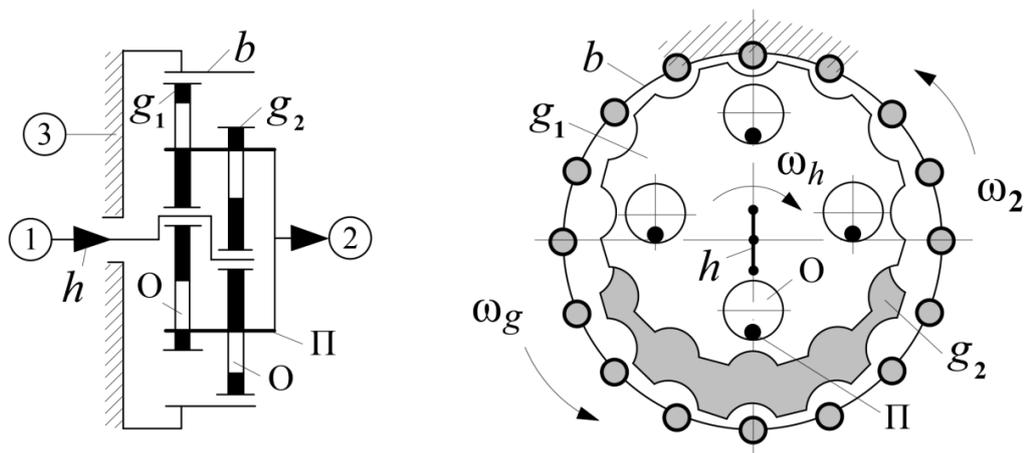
Планетарно-кривошипный механизм цветочного зацепления с двумя оппозитными сателлитами (звездочками)
